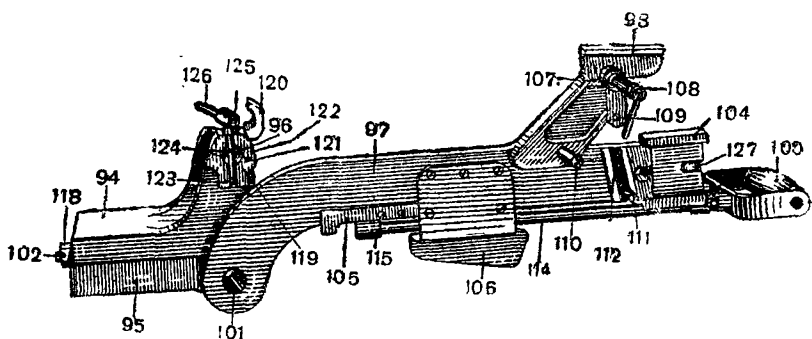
Нижний и верхний качающиеся столы (вид слева)
